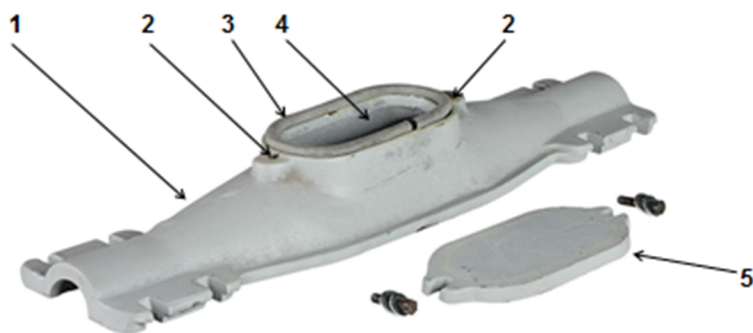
Детали верхней части корпуса муфты С-50 М удлиненной:
